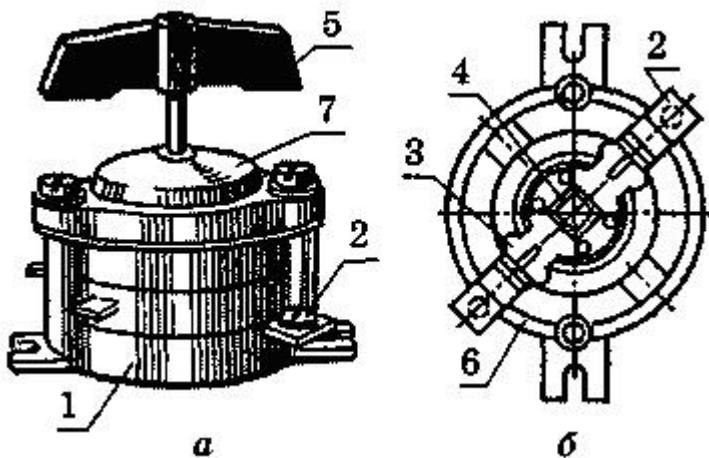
пакетный выключатель: а — общий вид; б — полюс (вид сверху); 1 — изоляционные секции (пакеты); 2 — неподвижные контакты; 3 — подвижные контакты; 4 — четырехгранный валик; 5 — рукоятка; 6 — фибрзовые шайбы; 7 — крышка.
